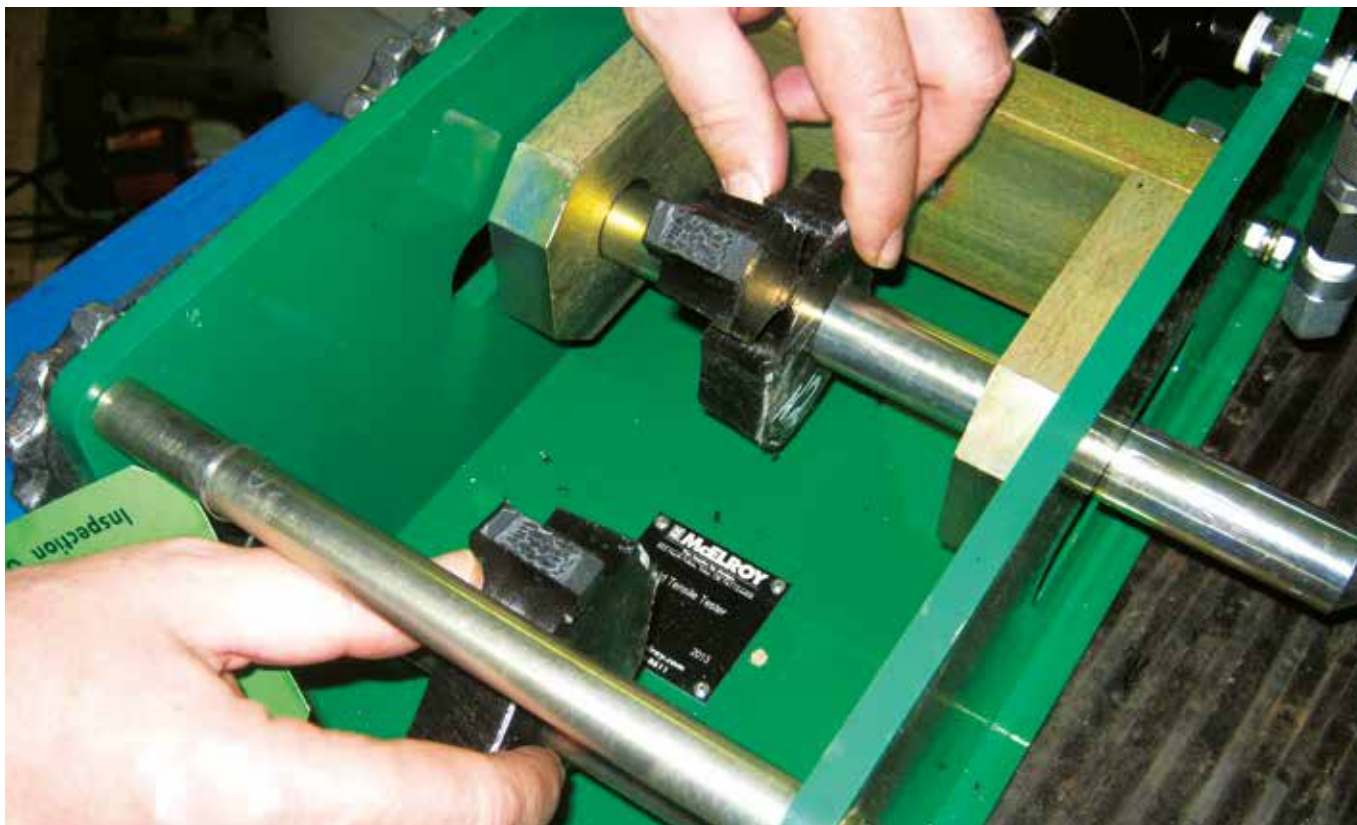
Хрупкое разрушение сварочного шва. Результат отрицательный.
